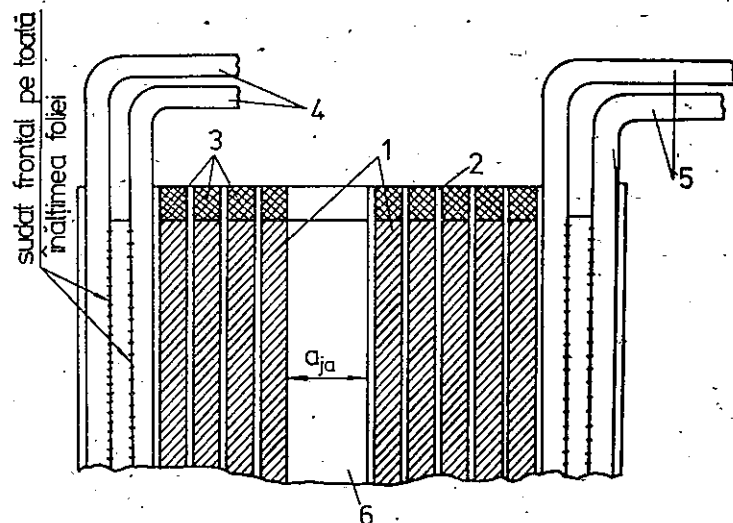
29. Înfășurare cilindrică stratificată din folie de Aluminiu:
